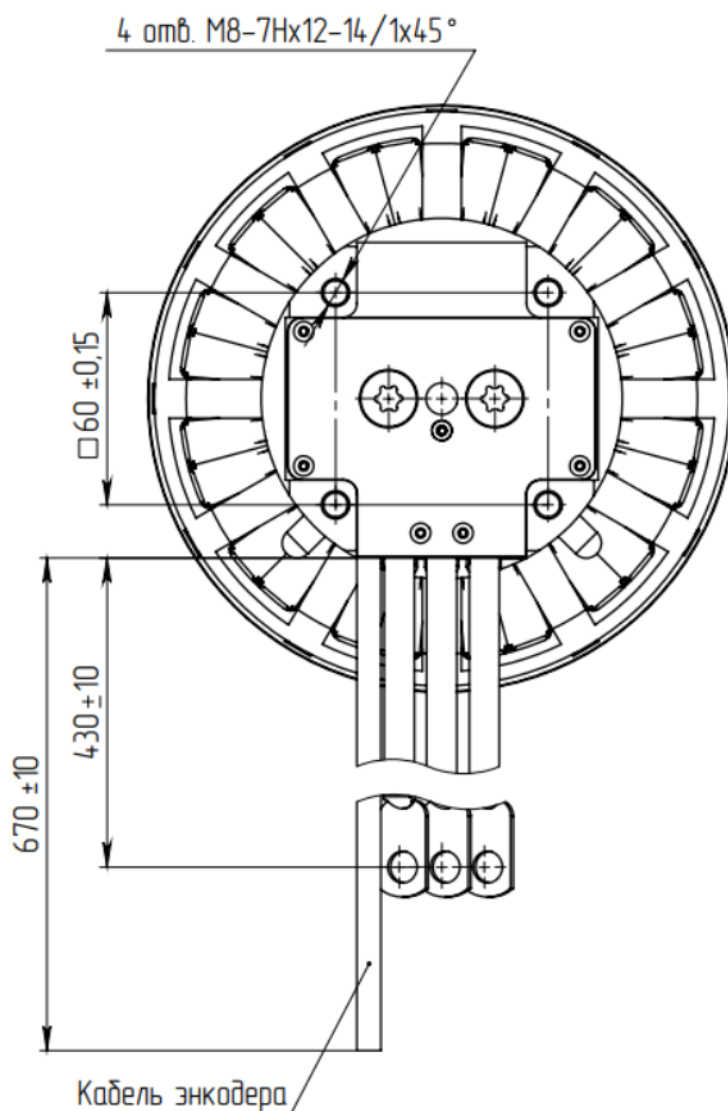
Присоединительные размеры изделия к несущей конструкции
